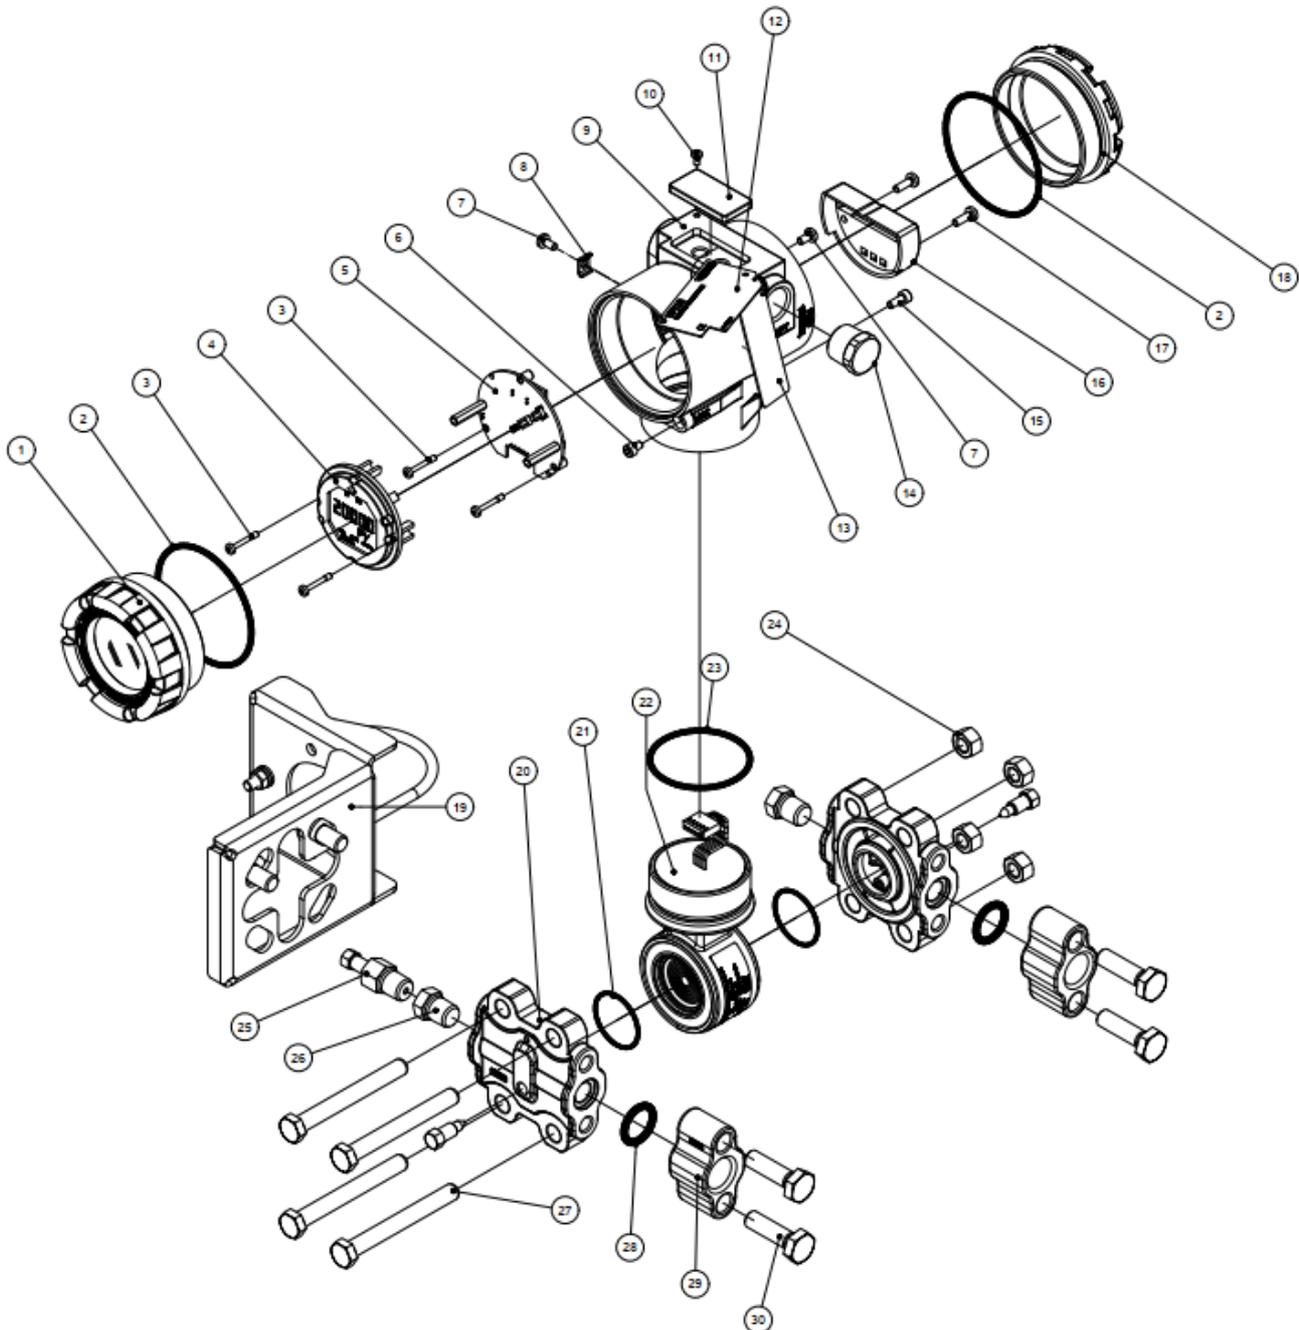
Desenho explodido do VPT10 HART padrão.
